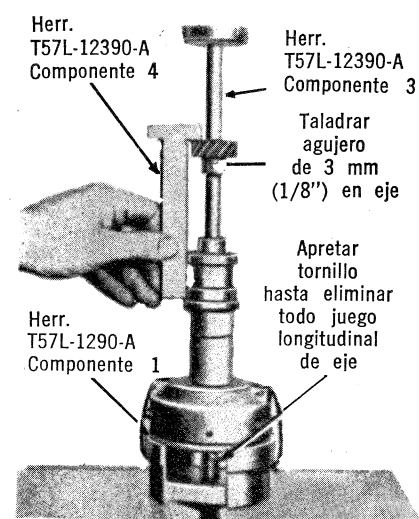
Instalación de Engranaje y Eje Nuevos. Típico.
